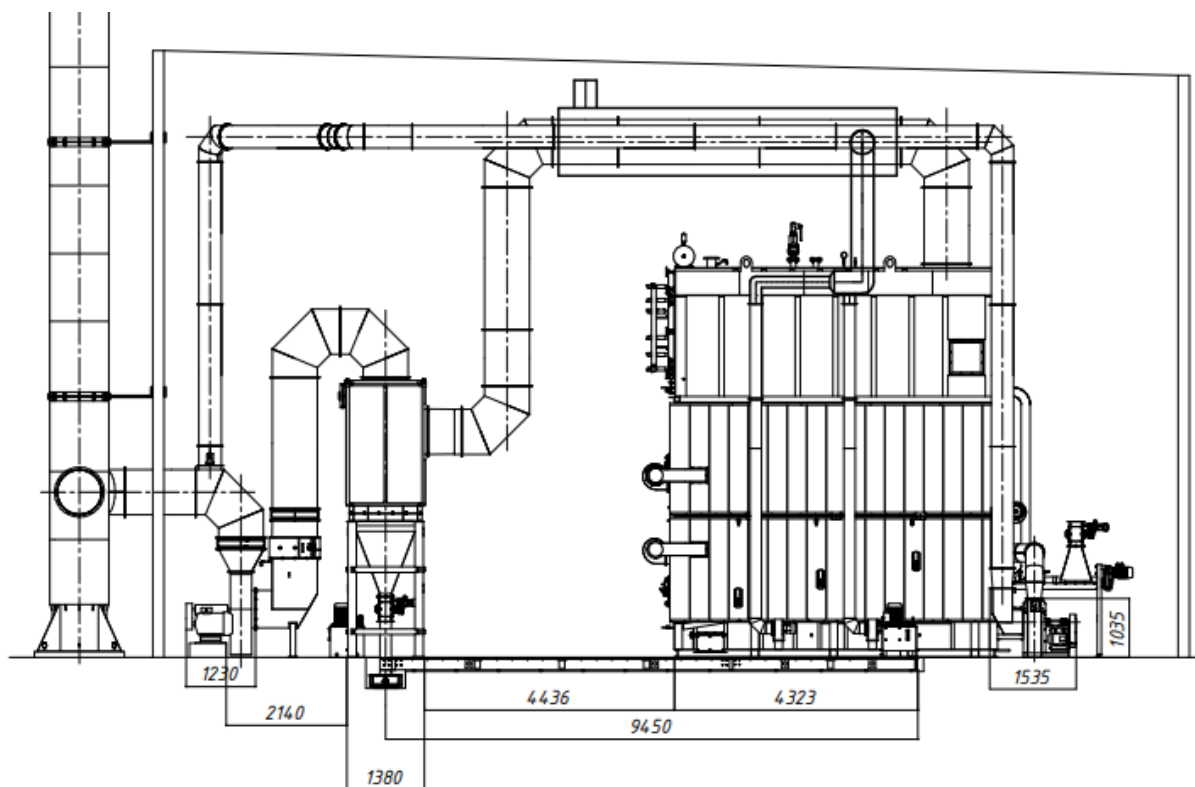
Общий вид котлоагрегата Гейзер TERMOWOOD кВт 4000Т с воздухоподогревателем
